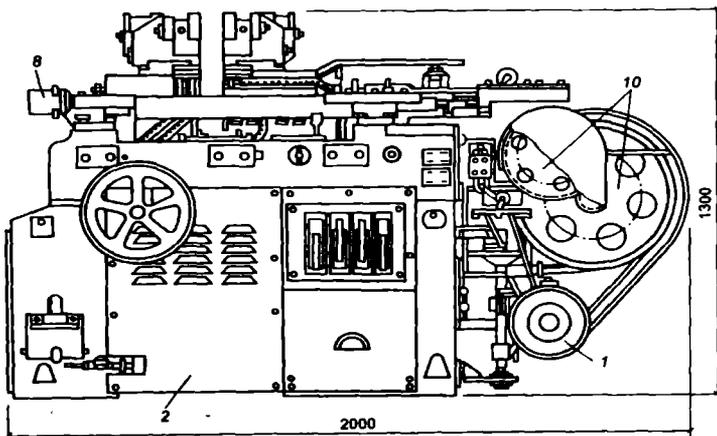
Машина МС-2008 (МСМУ-150) для стыковой сварки:
